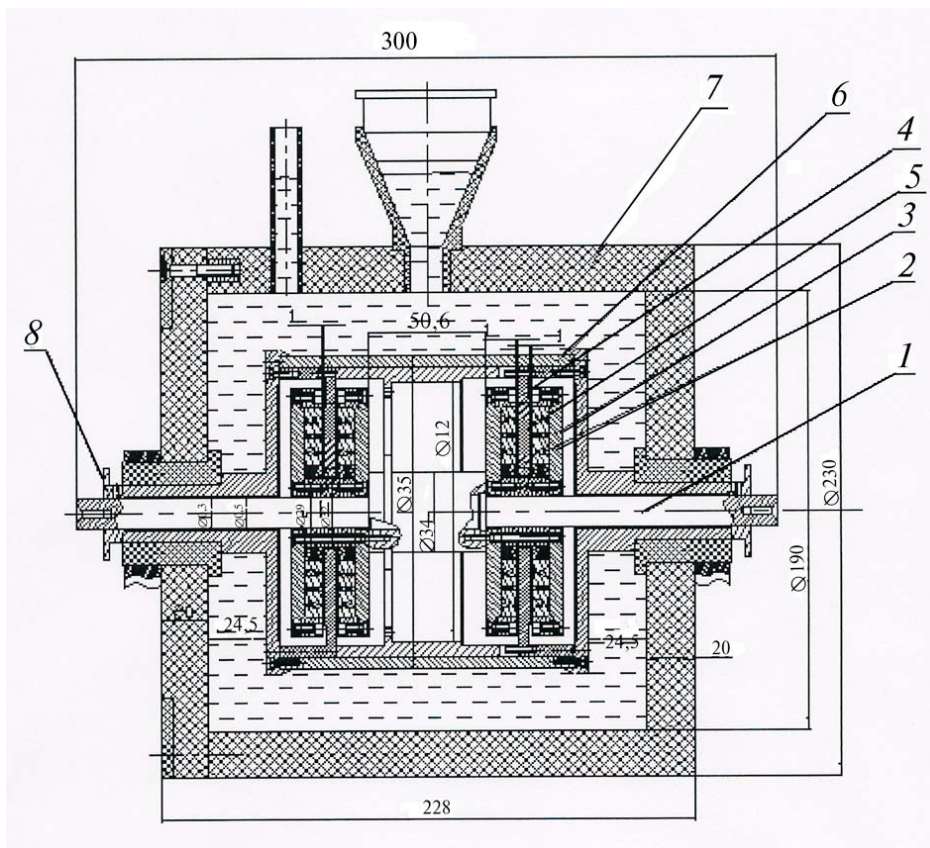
Сборочный чертеж роторной системы на ВТСП-опорах:
